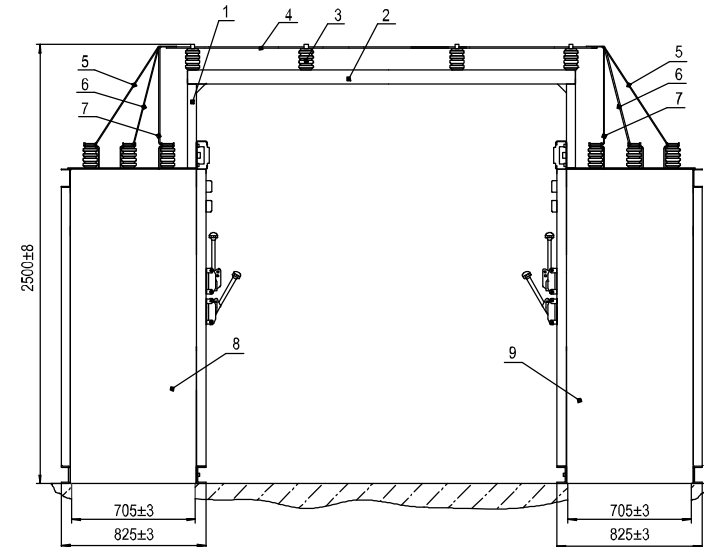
Габаритные, установочные, присоединительные размеры КСО-306 с шинным мостом:
